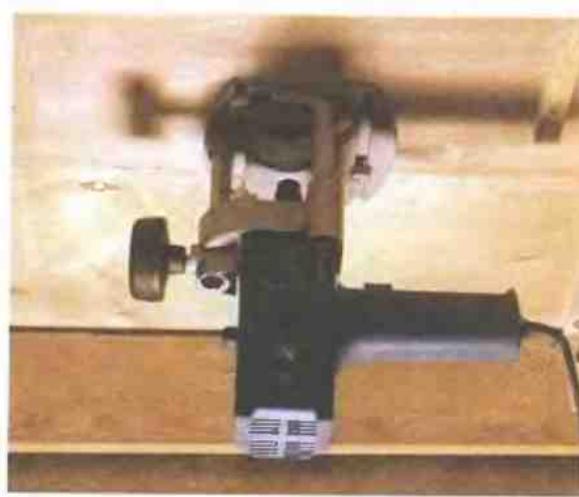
Ручной фрезер. Крепление к нижней поверхности рабочего стола
